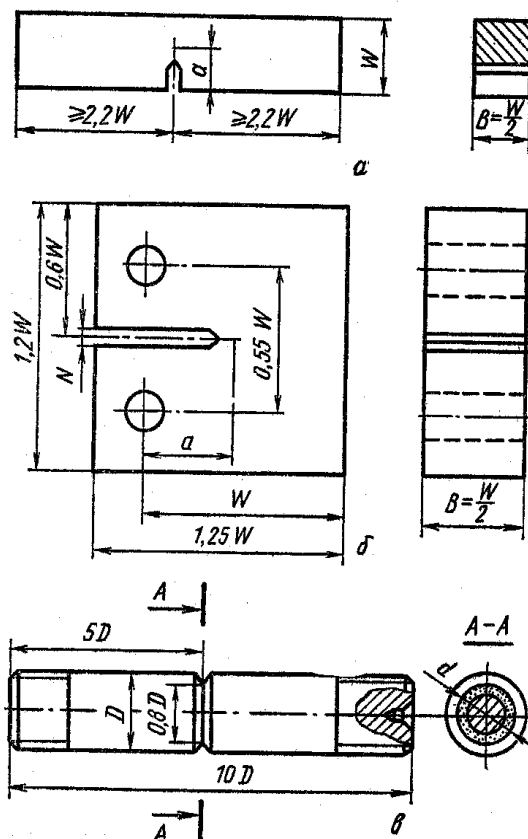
Типы образцов для определения K_{Ic} и соотношения их размеров: a – для испытаний на изгиб: b – для испытаний на внецентренное растяжение: c – цилиндрический образец для испытаний на растяжение
